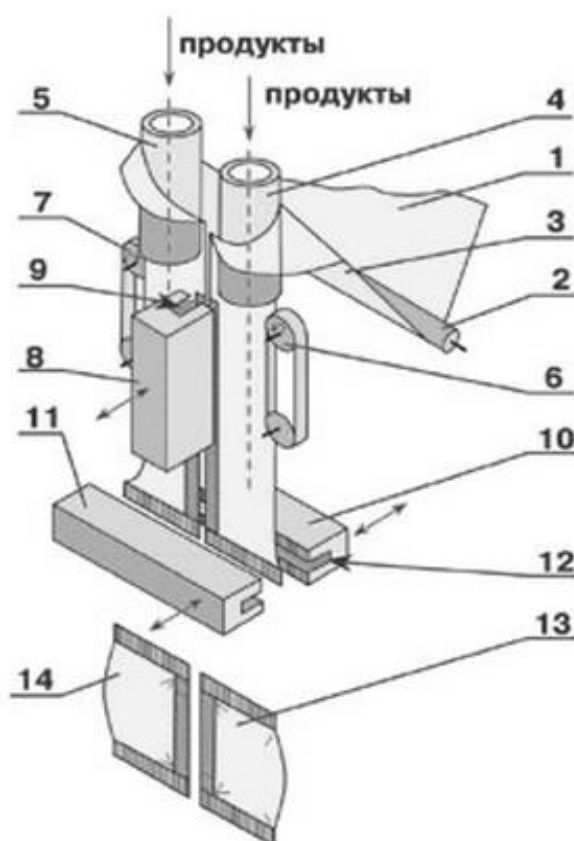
Схема двохпотокової машини із комірцем періодичної дії, з протягуючими транспортерами: 1 – пакувальний матеріал; 2 – направляючий ролик; 3 – комірець; 4, 5 – продуктопровід; 6, 7 – механізм протяжки; 8 – поздовжнє зварювання; 9, 12 – ніж; 10, 11 – поперечно-зварювальні головки; 13, 14 – споживча упаковка.
